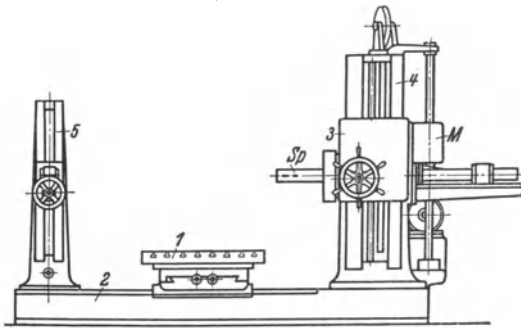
Waagrecht-Bohr- und Fräsmaschine.
